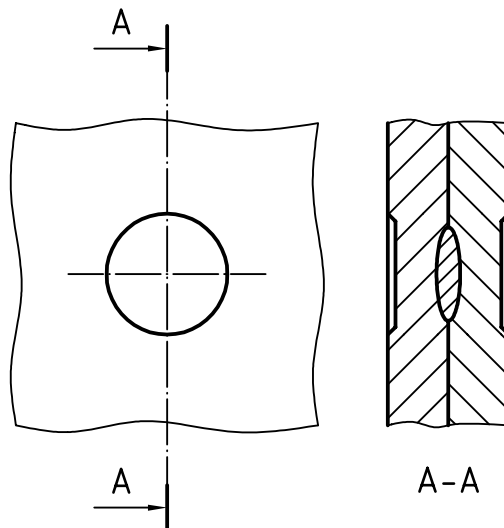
Positions recommandées pour prélever des sections dans des éprouvettes: soudure circulaire
